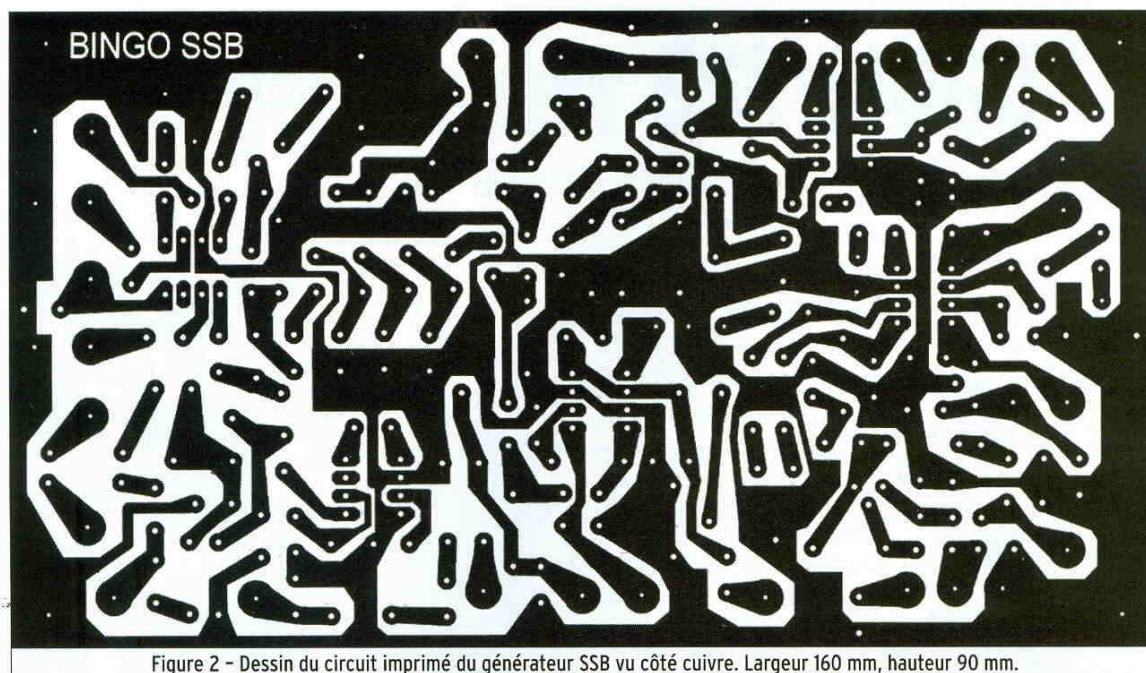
Dessin du circuit imprimé du générateur SSB vu côté cuivre. Largeur 160 mm, hauteur 90 mm.
